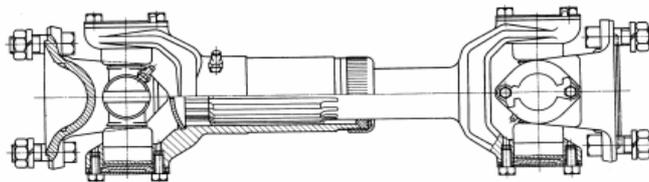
Общий вид карданного вала с шарнирами неравных угловых скоростей
